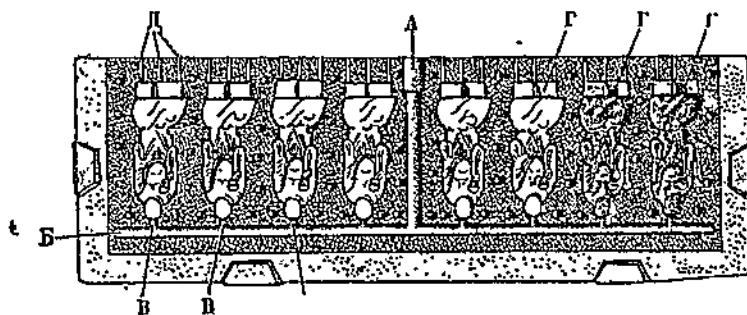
Отливка „под давлением“. Форма для одновременной отливки восьми статуэток. Отливки, лежащие в заливной половине формы: А—литник, Б—общий канал, В—остротки канала, Г—крестовидная пластиника, Д—воздушные каналы. Крестовидная пластиника Г, приделанная к модели статуэтки, образует форму углубления, в котором собирается воздух, вытесняемый из формы гипсом; из этого углубления воздух через воздушные канальчики выходит наружу. При отсутствии крестовидной пластиинки воздух не мог бы быть удален из формы через узенькие воздушки и на основании отливка образовались бы многочисленные пузырьки.
